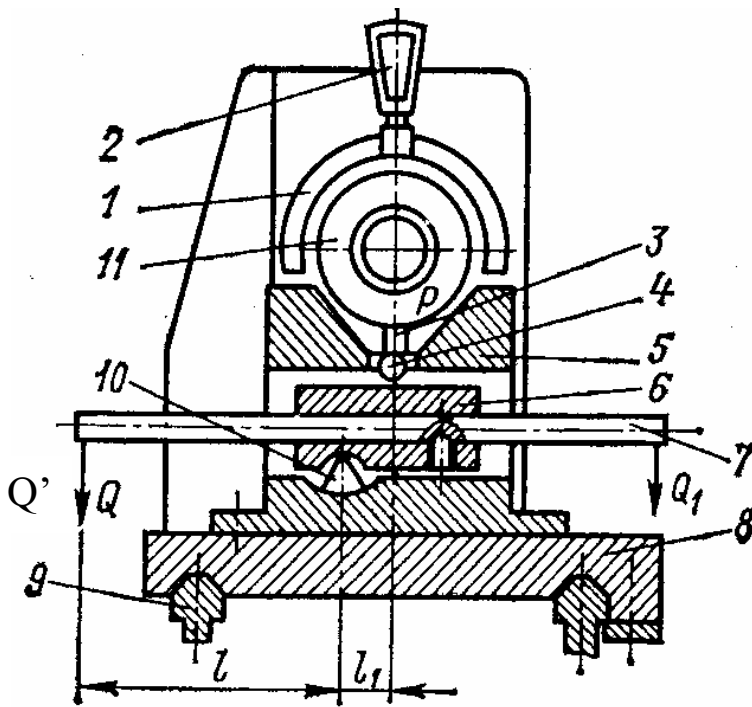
Пристрій для визначення зазору в передньому підшипнику шпинделя: 1 – скоба; 2 – індикатор; 3 – натискний палець; 4 – кулька; 5 – призма; 6 – втулка; 7 – важіль; 8 – основа; 9 – станина верстата; 10 – ніж; 11 – шпиндель верстата
